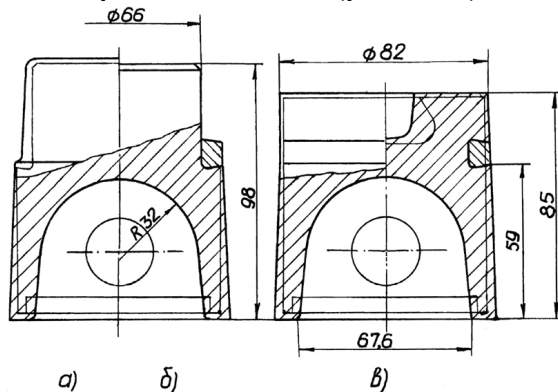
Технологические переходы штамповки биметаллической заготовки поршня энергоагрегата
